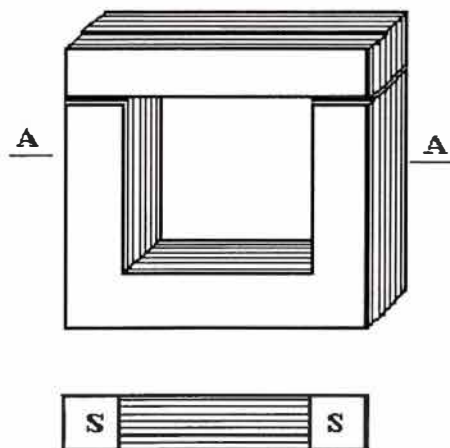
Vista y corte de un núcleo tipo núcleo
